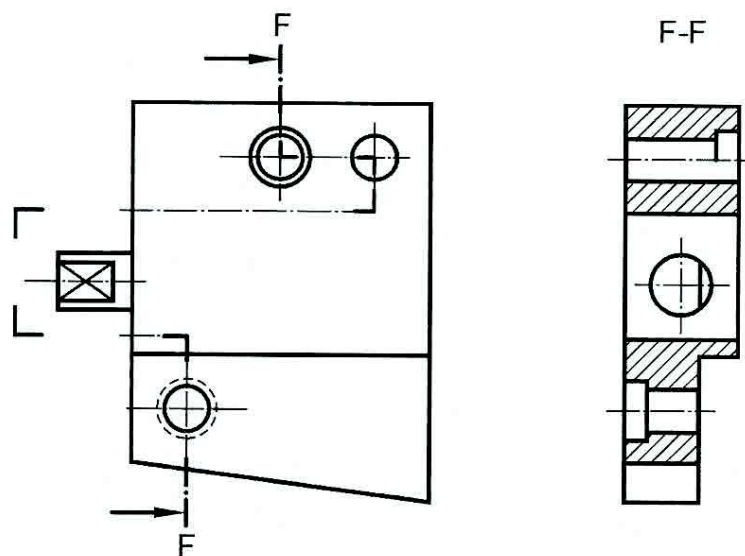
Plano de corte posicionado parcialmente fuera del objeto
